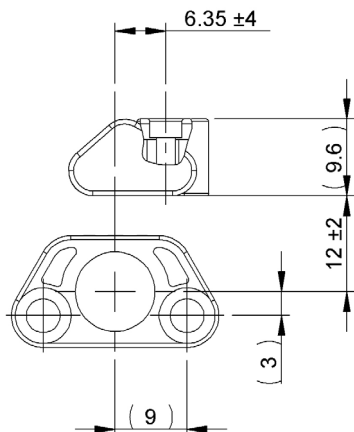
Distâncias com indicador de posição BAM TG-MP-028
